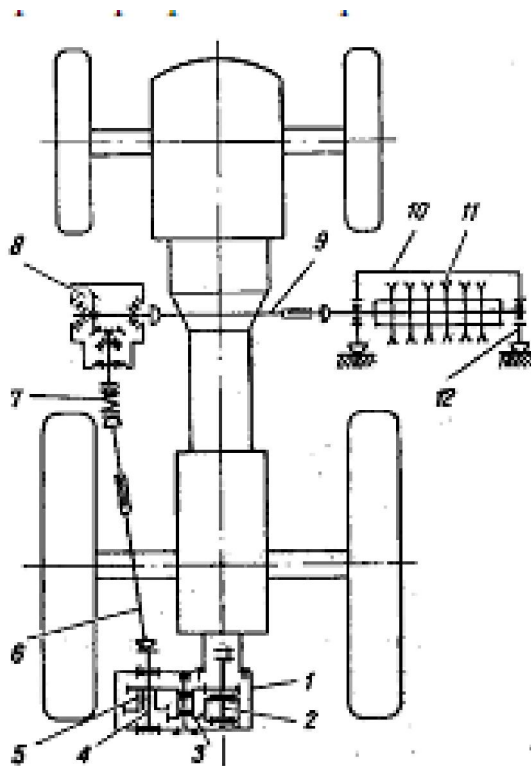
Фреза садова ФСН-0,9Г: 1- циліндричний редуктор; 2 - верхній вал; 3 - проміжний блок; 4 - нижній вал; 5 - блок шестерень; 6 - повздовжній карданний вал; 7 -запобіжна муфта; 8 - конічний редуктор; 9 - поперечний карданний вал; 10 - кожух барабана; 11 - диск барабана; 12 - опорний полозок.
